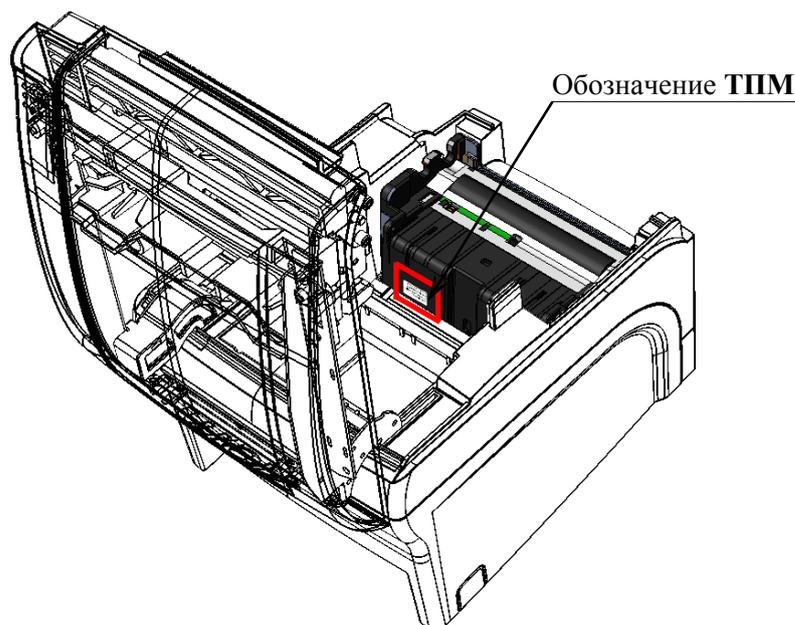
Расположение наклейки с обозначением ТПМ.
